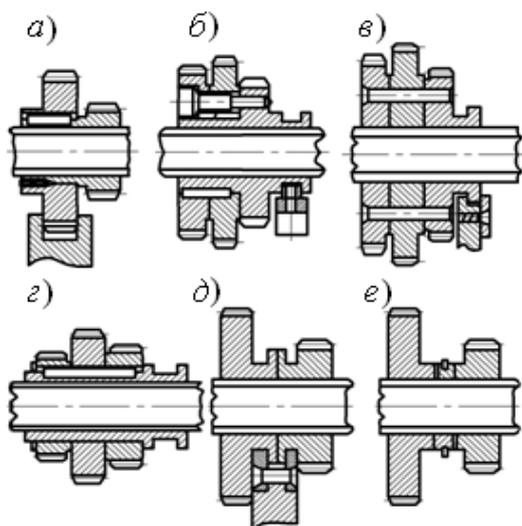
Конструкции составных блоков зубчатых колес
